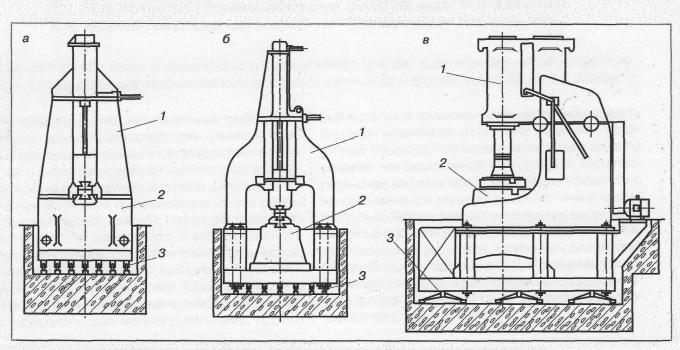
Конструктивные схемы виброизолирующих установок кузнечных молотов: a — штамповочный; b — ковочный пневматический; t — станина молота; t — шабот; t — рессоры
